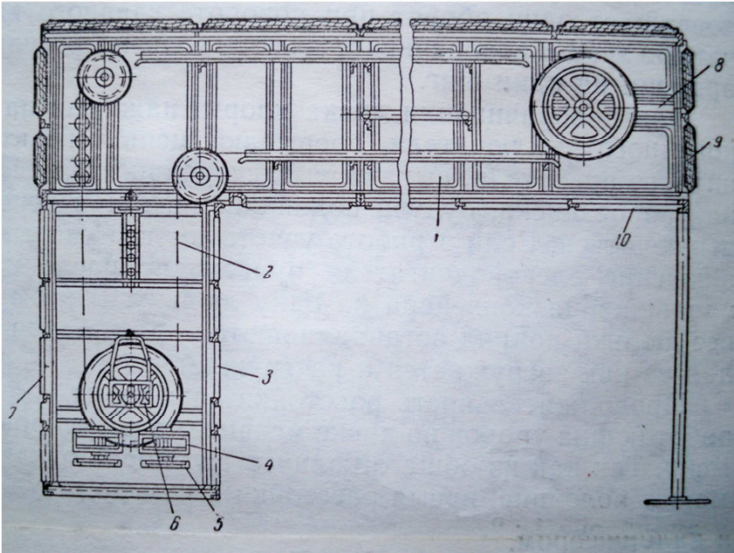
Конвеєрна шафа остаточного розстоювання тістових заготовок: 1 – корпус шафи на кутниковому каркасі; 2 – ланцюговий двониточний люльковий конвеєр; 3 – вивантажувальне вікно шафи; 4 – люльки поміж двома стрічками конвеєра; 5 – полки люльок завширшки 1900 мм; 6 – привідний ланцюговий блок – вал з двома ланцюговими та привідною зірочками (крок зубців та ланок ланцюгів 140 мм); 7 – завантажувальне вікно шафи; 8 – пристрій натягування ланцюгів; 9, 10 – щити обшивки шафи
